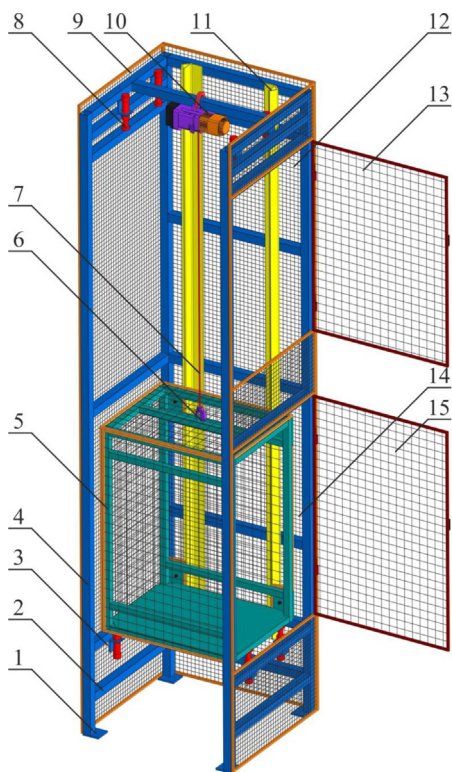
3D модель конструкції клітьової підйомної установки (вид спереду, ліворуч) 1) – з'єднувальна опора; 2) – горизонтальна ферма; 3) – буфер нижній; 4) – вертикальна ферма; 5) – кліть; 6) – вантажний гак; 7) – канат; 8) – буфер верхній; 9) – захисне загородження; 10) – електроталь; 11) – напрямні рейки; 12) – вихід на 2-й поверх; 13) – двері 2-го поверху; 14) – вихід на 1-й поверх; 15) – двері 1-го поверху
